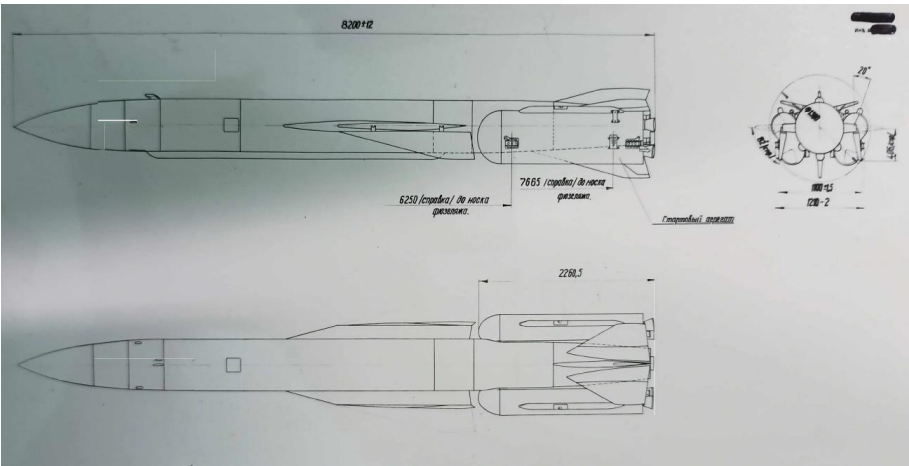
Габаритный чертеж ракеты «Аметист» со стартовым агрегатом
